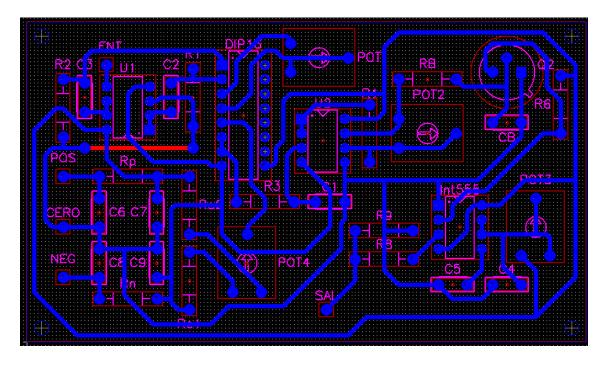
Diseño PCB del calibrador de cronómetros por medio de inducción.
